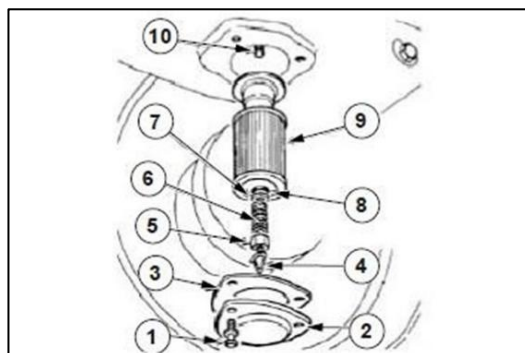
VUE ÉCLATÉE DU FILTRE D'ASPIRATION
